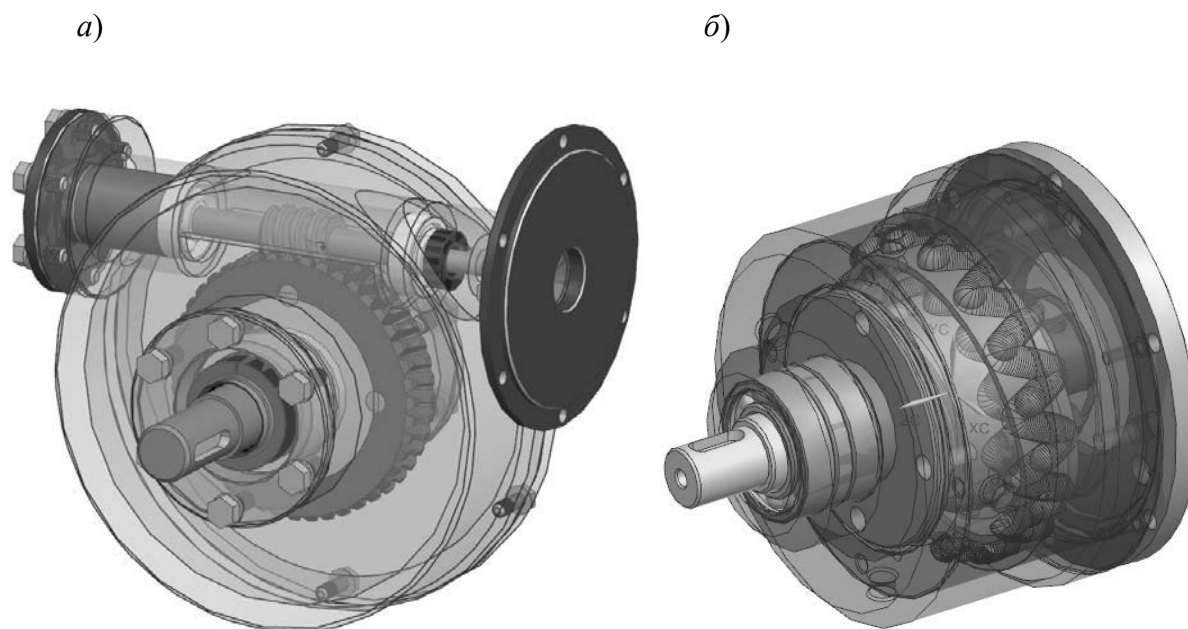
Модели редукторных узлов: а – с червячной передачей; б – с СРП
